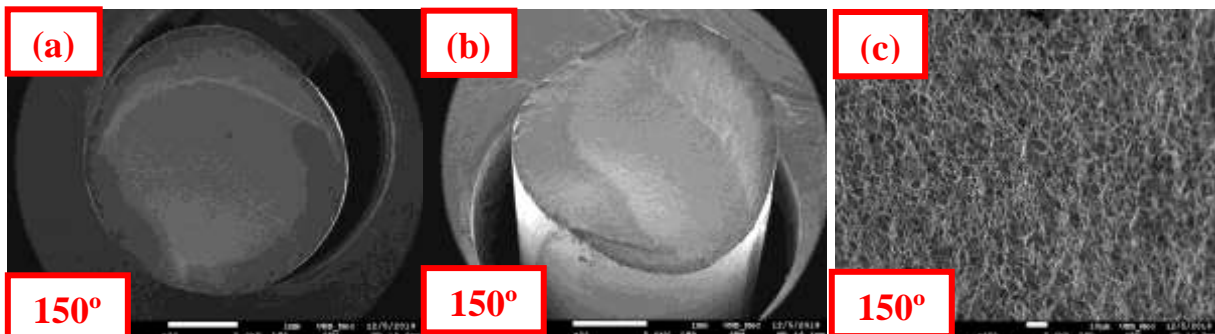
(a) Topo de superfície fraturada em ensaio a 150°C, (b) Zonas de propagação da trinca em superfície fraturada em ensaio a 150°C e (c) Dimples em superfície fraturada em ensaio a 150°C
